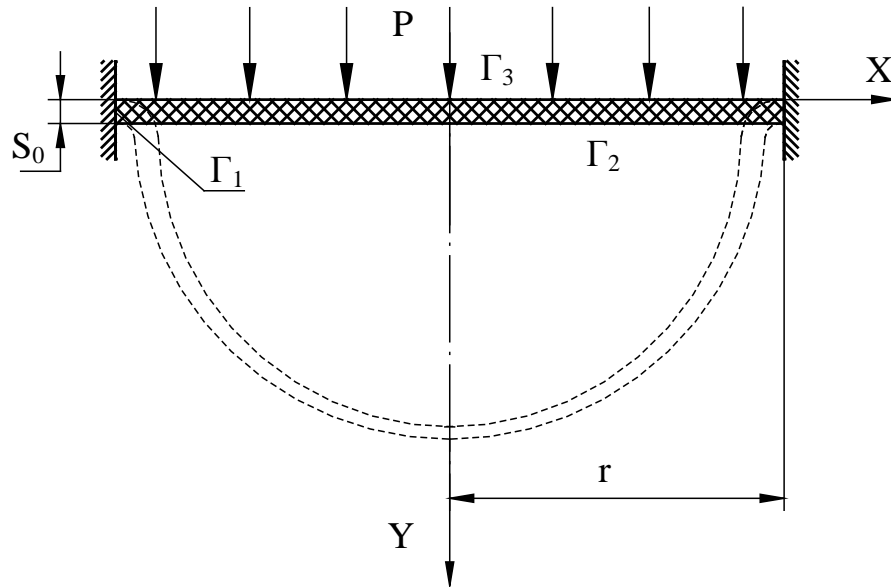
Расчетная схема процесса свободной формовки круглой заготовки с закрепленным фланцем
